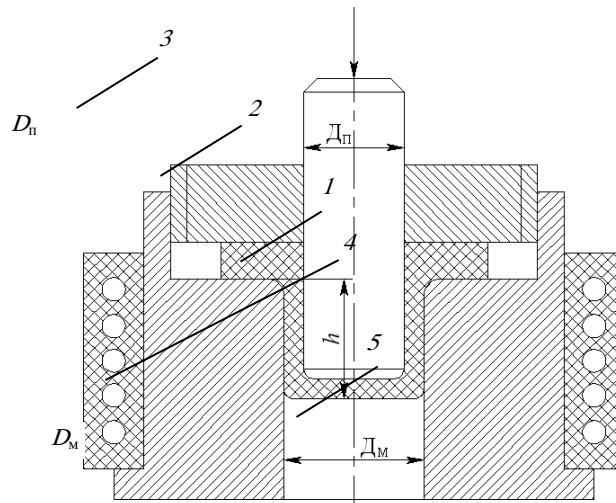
Схема испытательной пресс-формы для листовой штамповки с глубокой вытяжкой термопластов:
